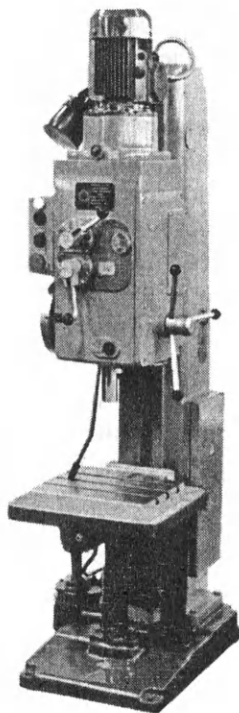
Вертикально-сверлильный станок МН25Н
